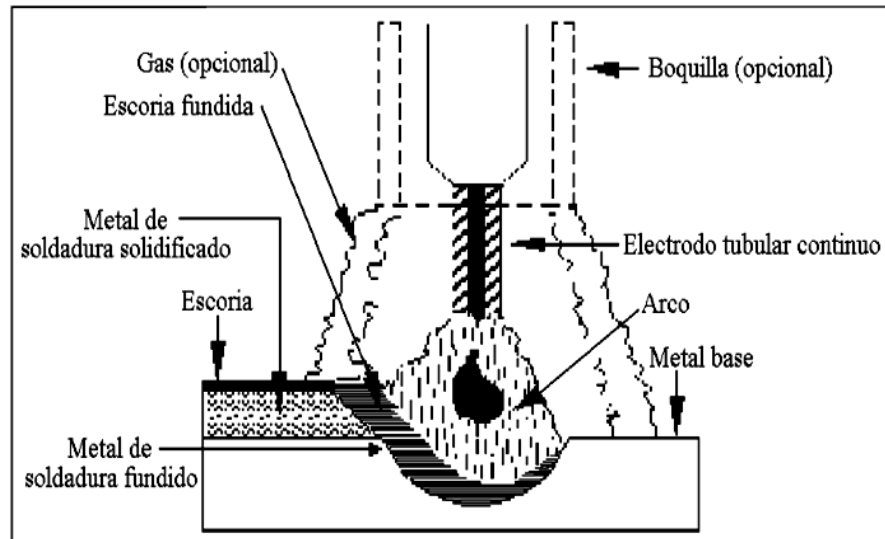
PROCESO DE SOLDADURA POR ARCO CON ELECTRODO TUBULAR CON NÚCLEO DE FUNDENTE FCAW (11)
